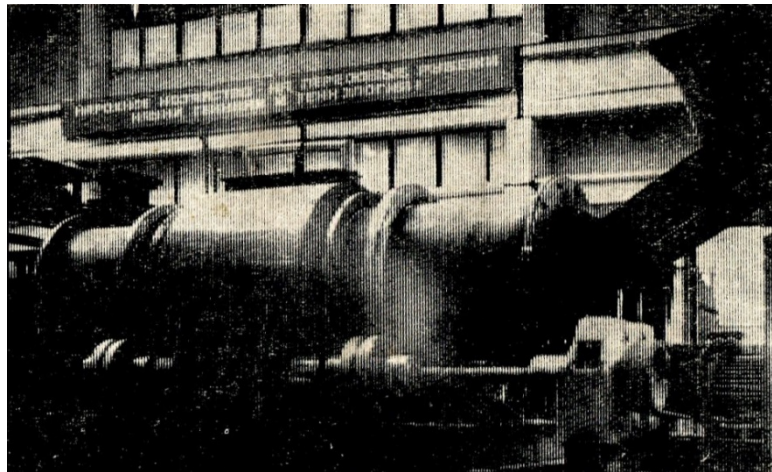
Барабан станка для непрерывной отделочно-зачистной обработки деталей в сборе с винтовым ротором
